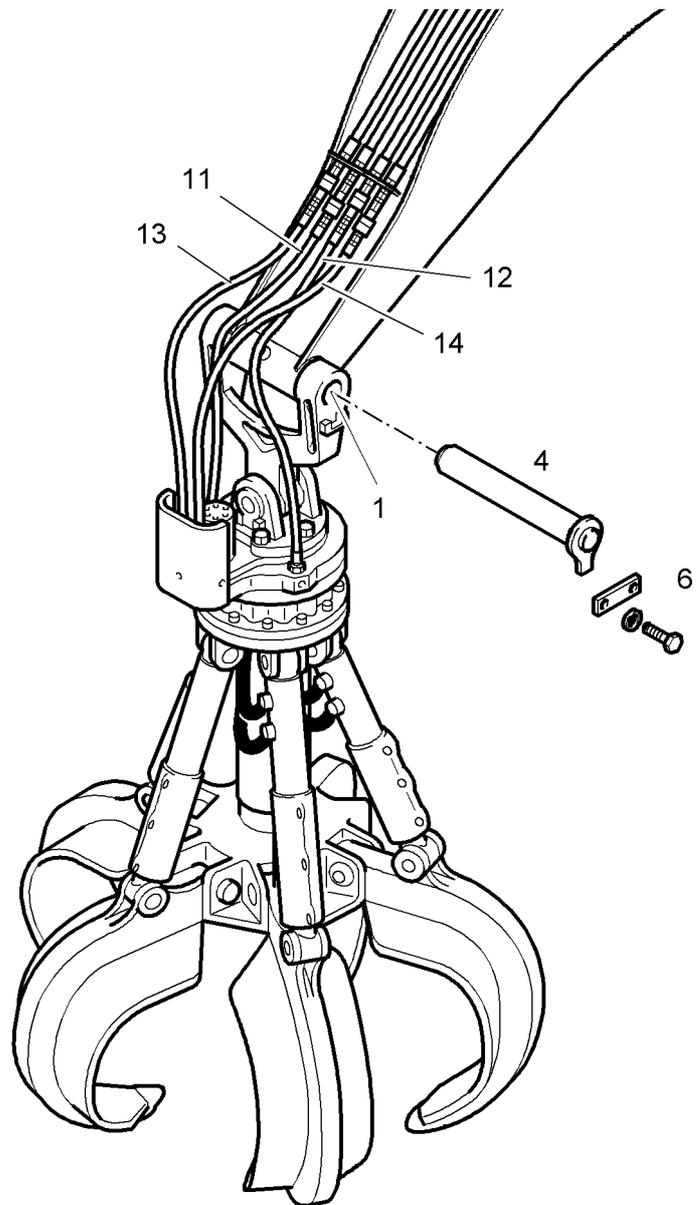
Montaje y desmontaje de la cuchara valva a nivel del balancín industrial
